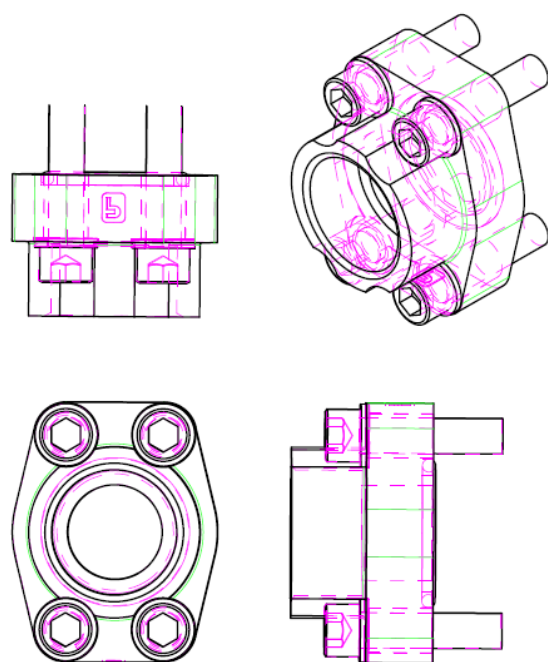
Vistas e isométrico Brida SAE soldada ISO 6162-1
